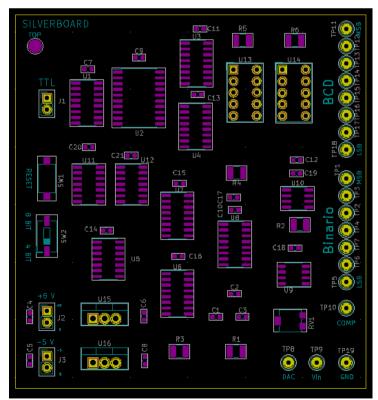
Colocación de componentes en la PCB con Pcbnew.
